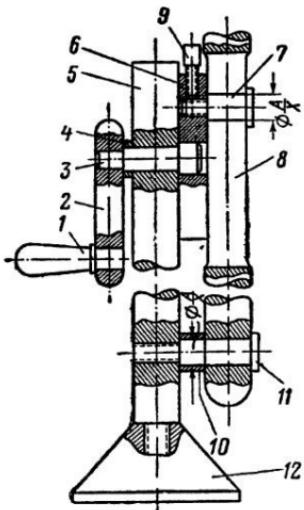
Элементарная модель кулисного механизма (схема соединения деталей).
